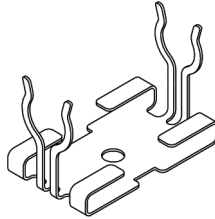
Montageclip (Befestigung mit M4-Schraube oder Kabelbinder)
